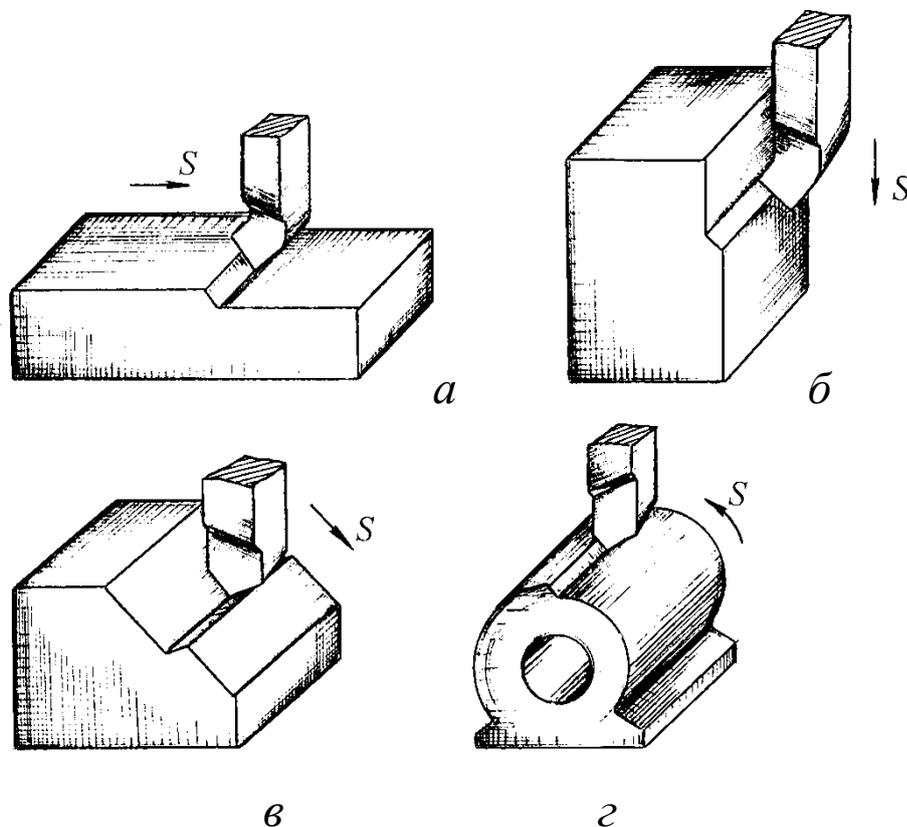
Схема обработки поверхностей на строгальных станках:
